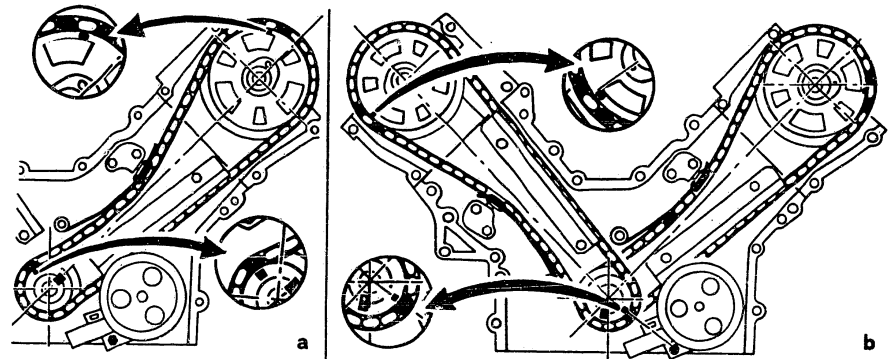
Motor Z7V: a) Stellung des Kurbelwellen- und Nockenwellenrades beim Einbau der linken Steuerkette – b) Einbau der rechten Kette.
